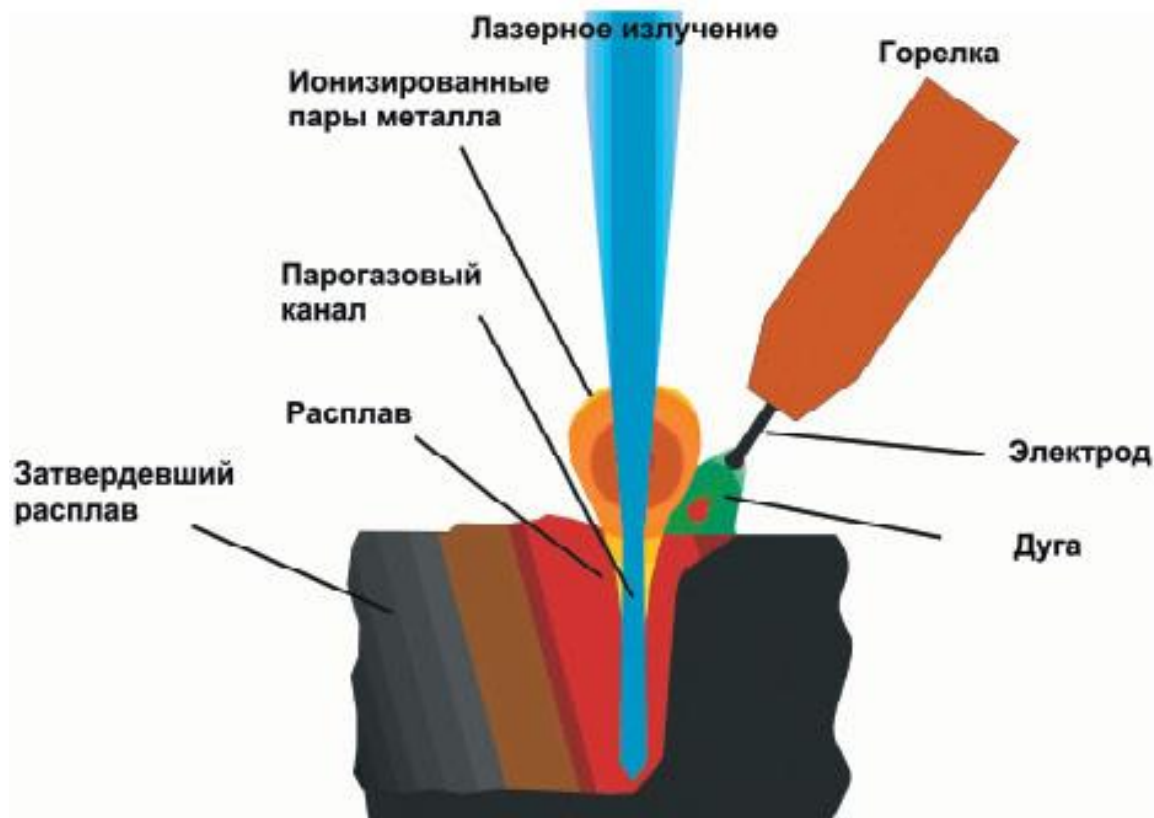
Схематическое изображение гибридной лазерно-дуговой сварки [99]
